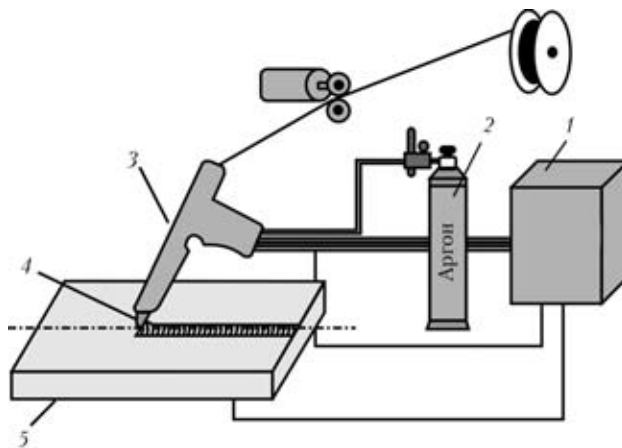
Схема процесса сварки МИГ: 1 — источник питания; 2 — защитный газ (аргон); 3 — горелка; 4 — присадочная проволока; 5 — алюминиевый образец
